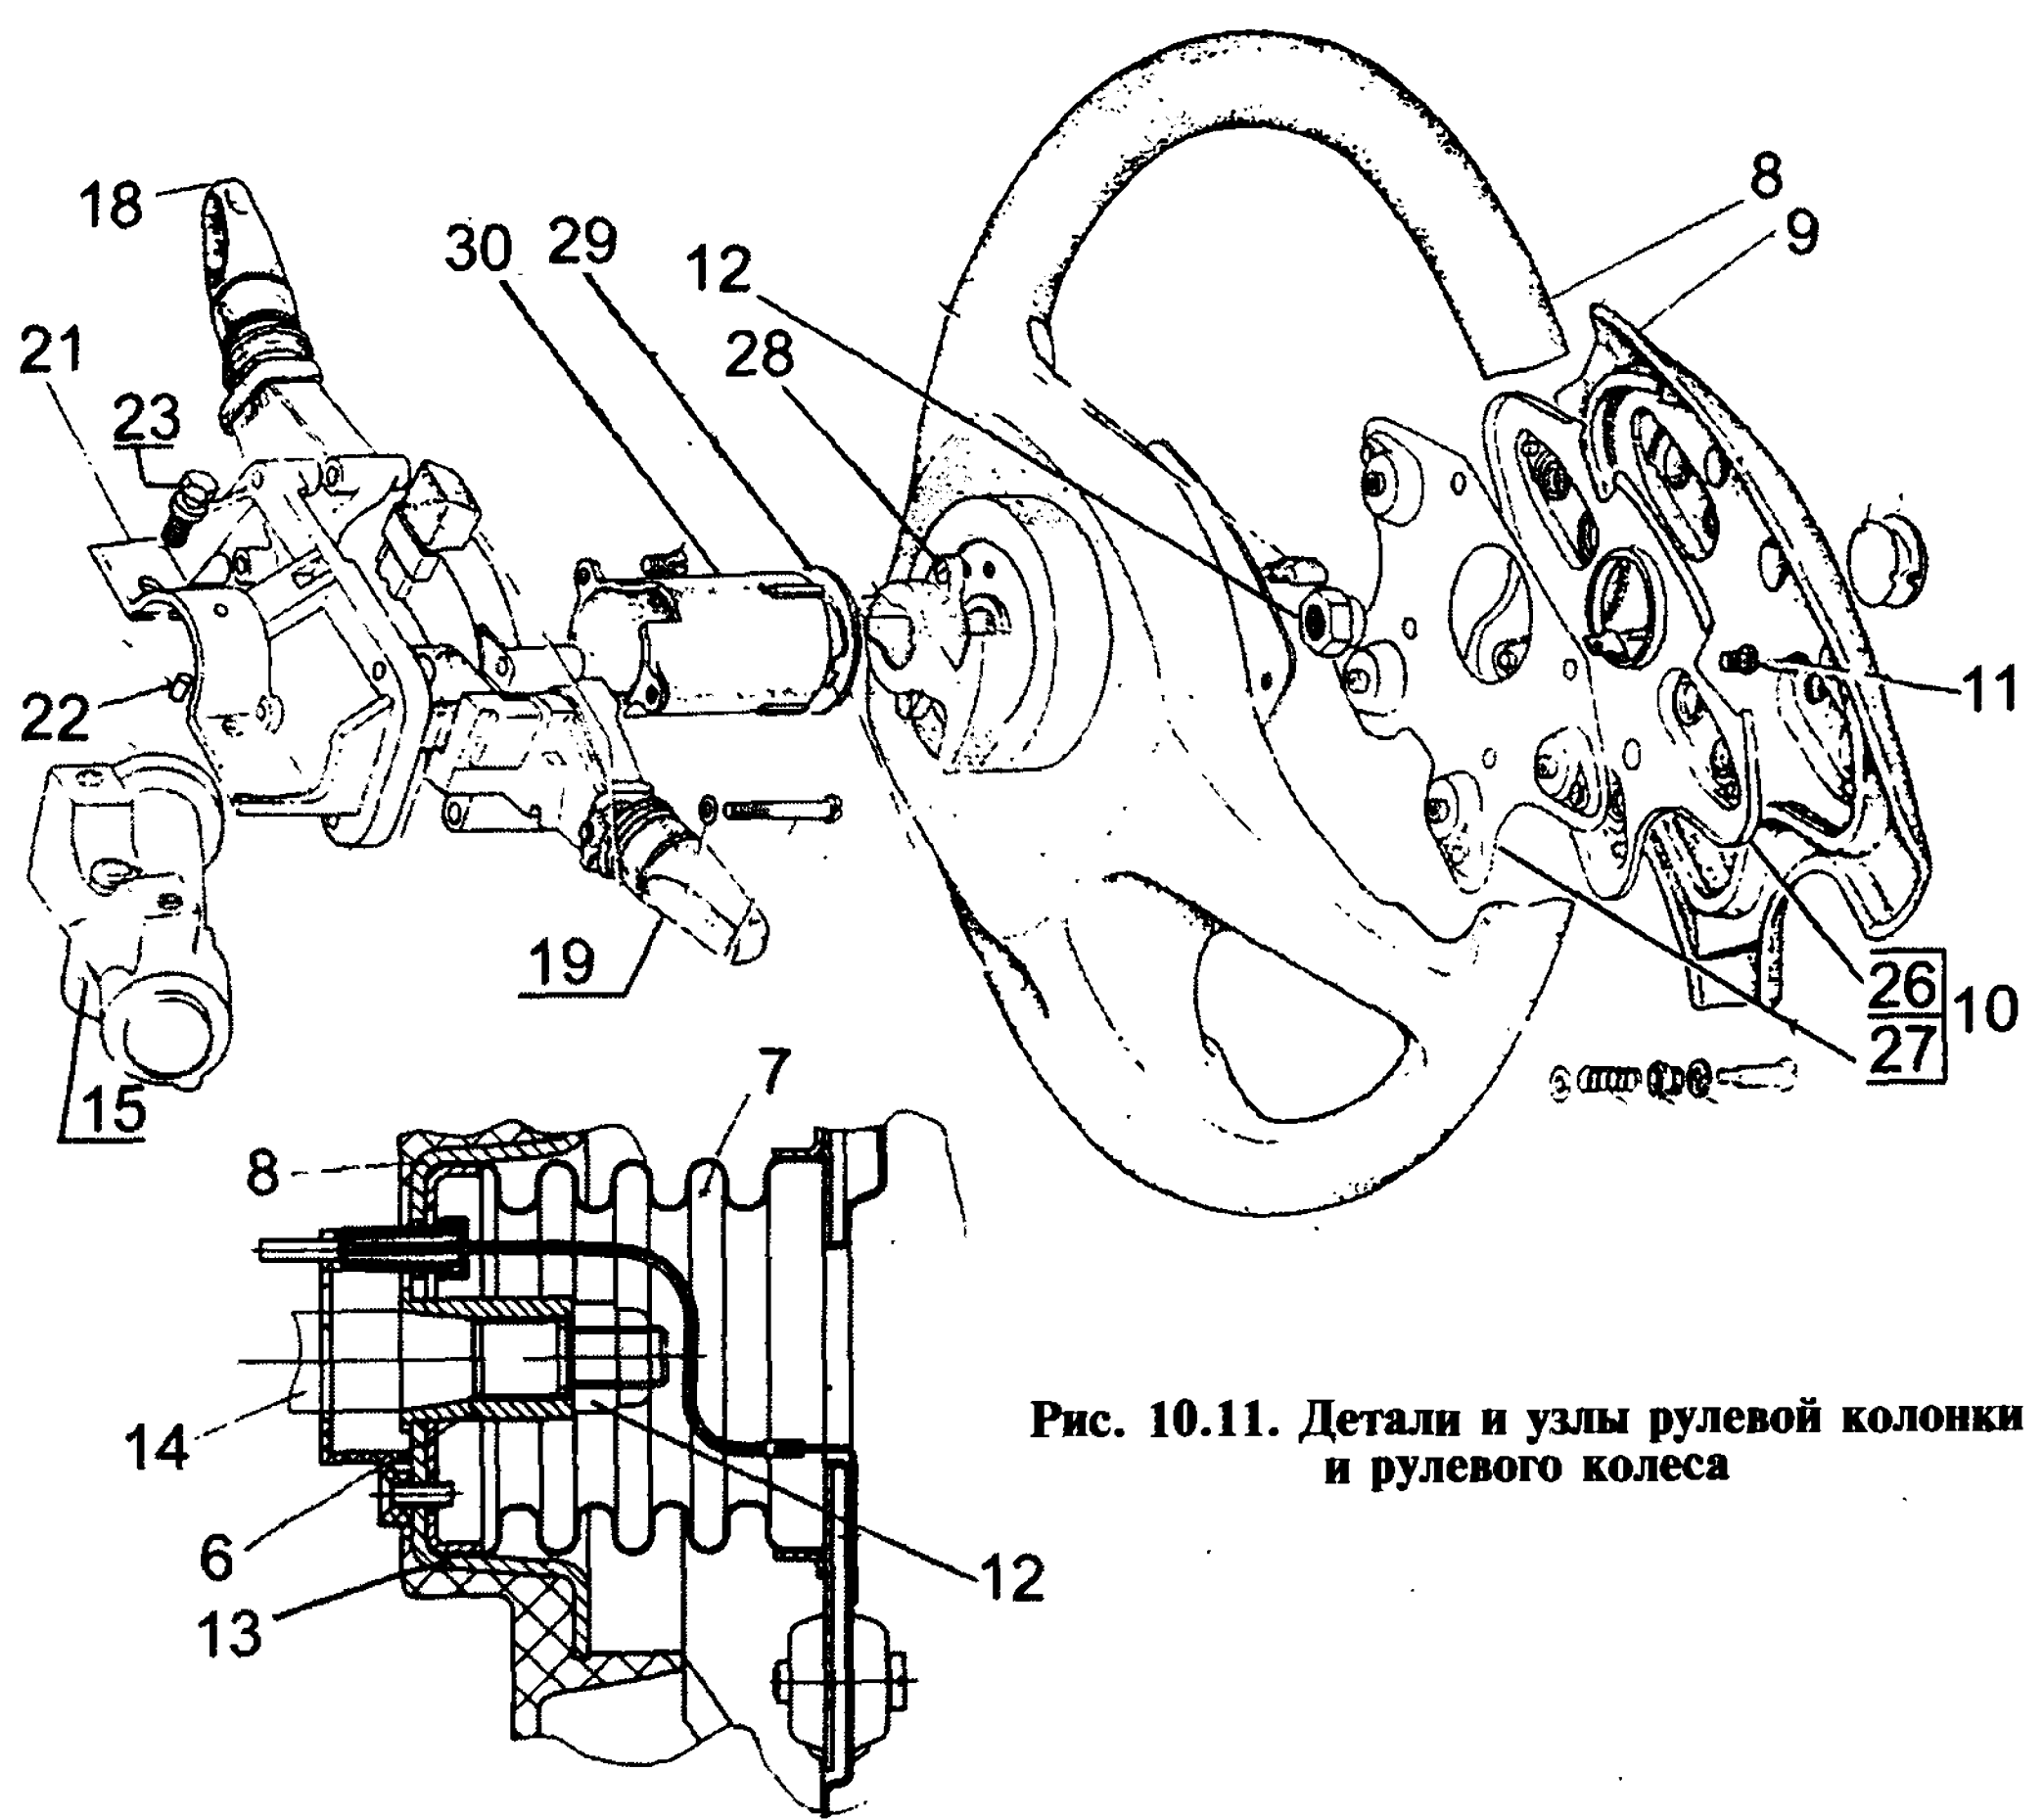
Детали и узлы рулевой колонки и рулевого колеса
